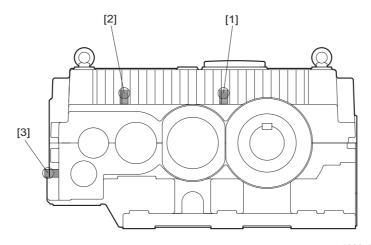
M3P.../M4P .. Posiciones de montaje de los adaptadores SPM M3P../M4P..
